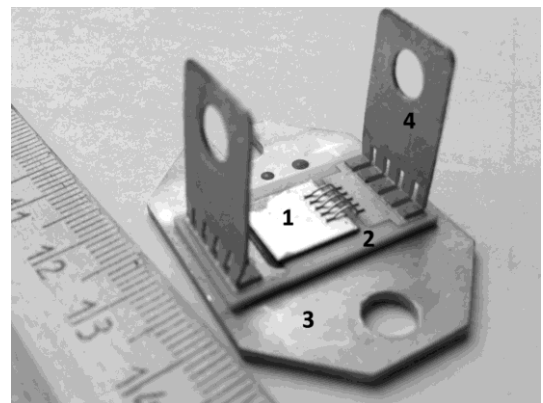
Внешний вид диода 2Д715 без крышки: 1 – кристалл; 2 – керамика; 3 – корпус; 4 – выводы
